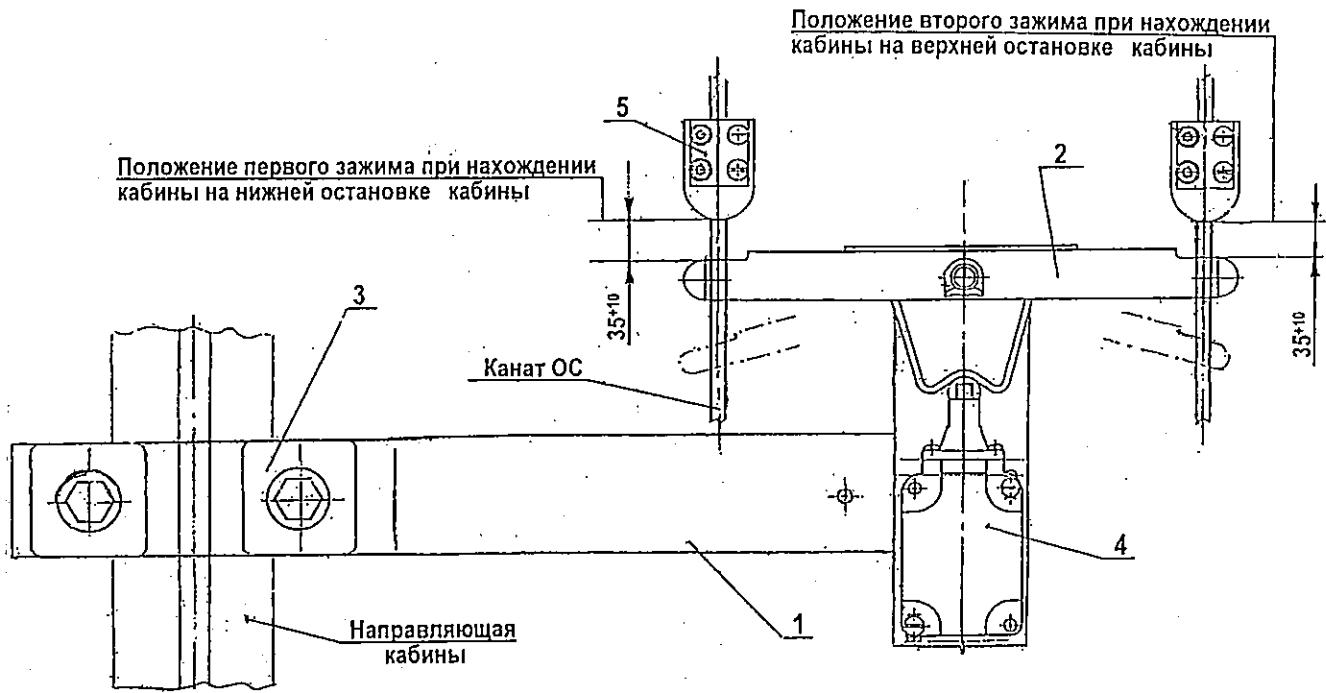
схемы сборок натяжного устройства каната ОС
